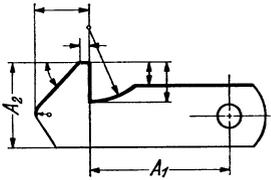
Sperrhaken. A_1 , A_2 = Ausgangsmaße für Formwerkzeug. Die zu fertigende Form ist dick ausgezogen.
